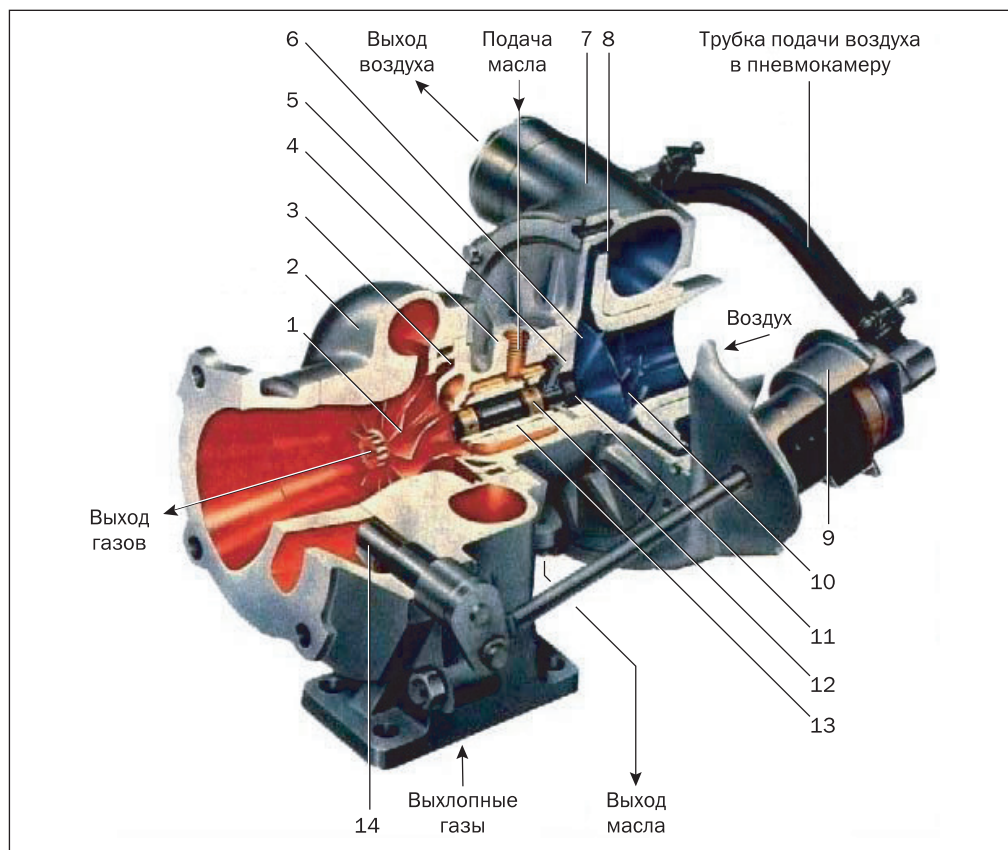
Турбокомпрессор Garrett: 1 — лопатки турбины; 2 — корпус турбины; 3 — тепловая защита; 4 — корпус подшипников; 5 — упор; 6 — защитная пластина; 7 — корпус компрессора; 8 — диффузор; 9 — пневмокамера управления заслонкой; 10 — колесо компрессора; 11 — уплотнение; 12 — подшипник; 13 — втулка подшипника; 14 — заслонка
